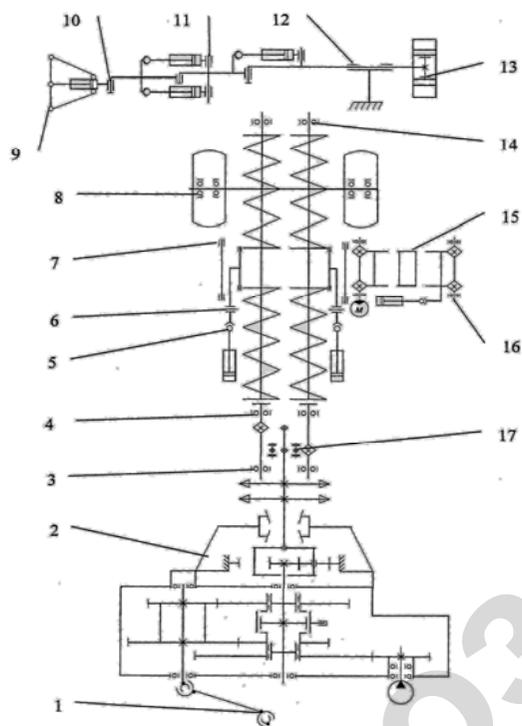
Точки смазки мобильного смесителя-раздатчика кормов:
